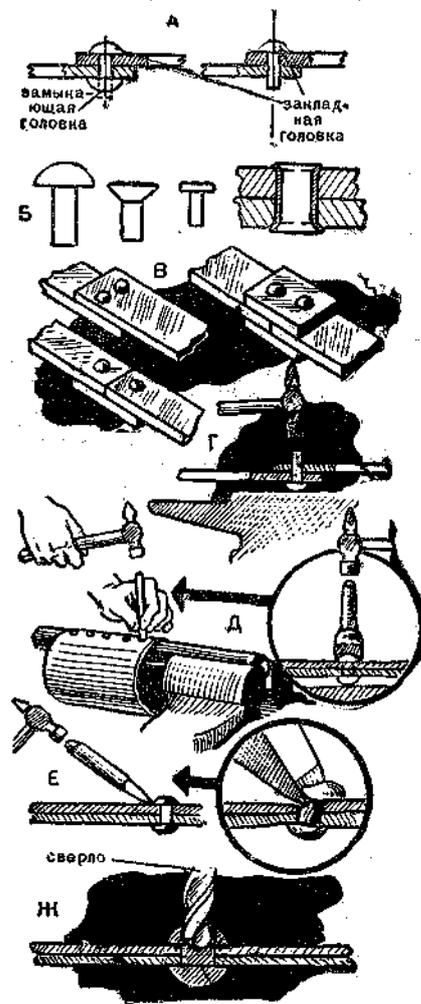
Соединения на заклепках: Л — заклепка и ее детали; В — виды заклепочных соединений; Г — установка заклепки; Д — использование обжимки; Е — срубание заклепки; Ж — высверливание заклепки,
